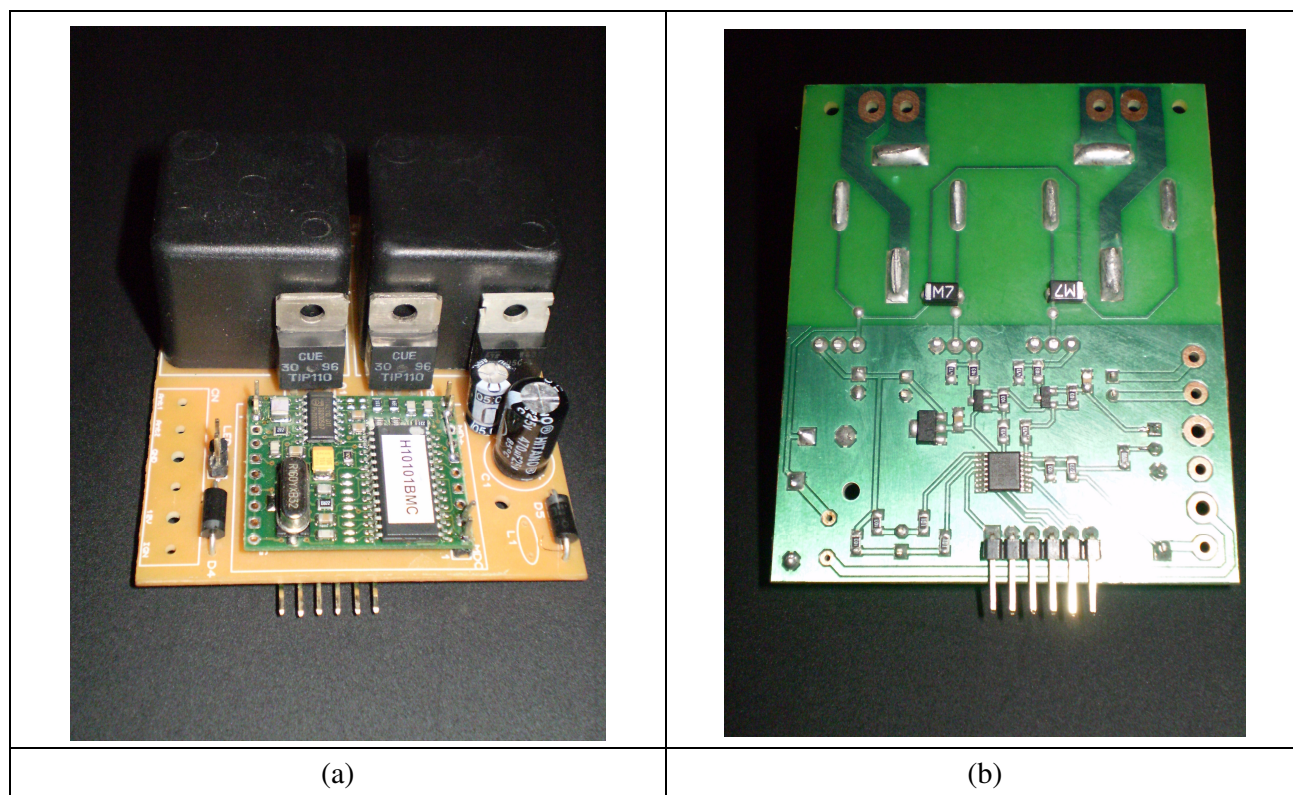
Placa MOTORFID: (a) Lado componentes; (b) Lado solda
